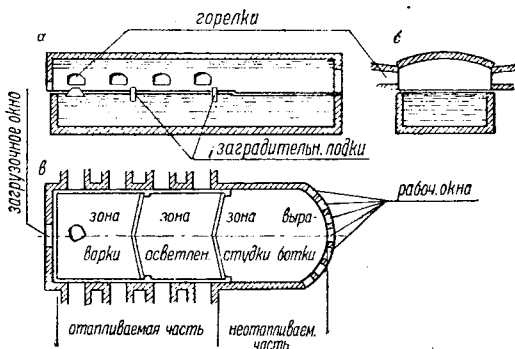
Схематический чертеж бассейна ванной печи непрерывного действия.
